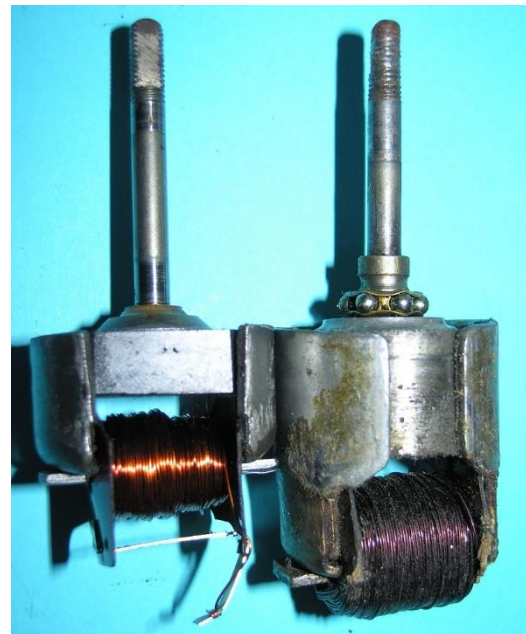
Gehäusedurchmesser: 46 mm, Dynamo und Generator, Gewicht 440 g
